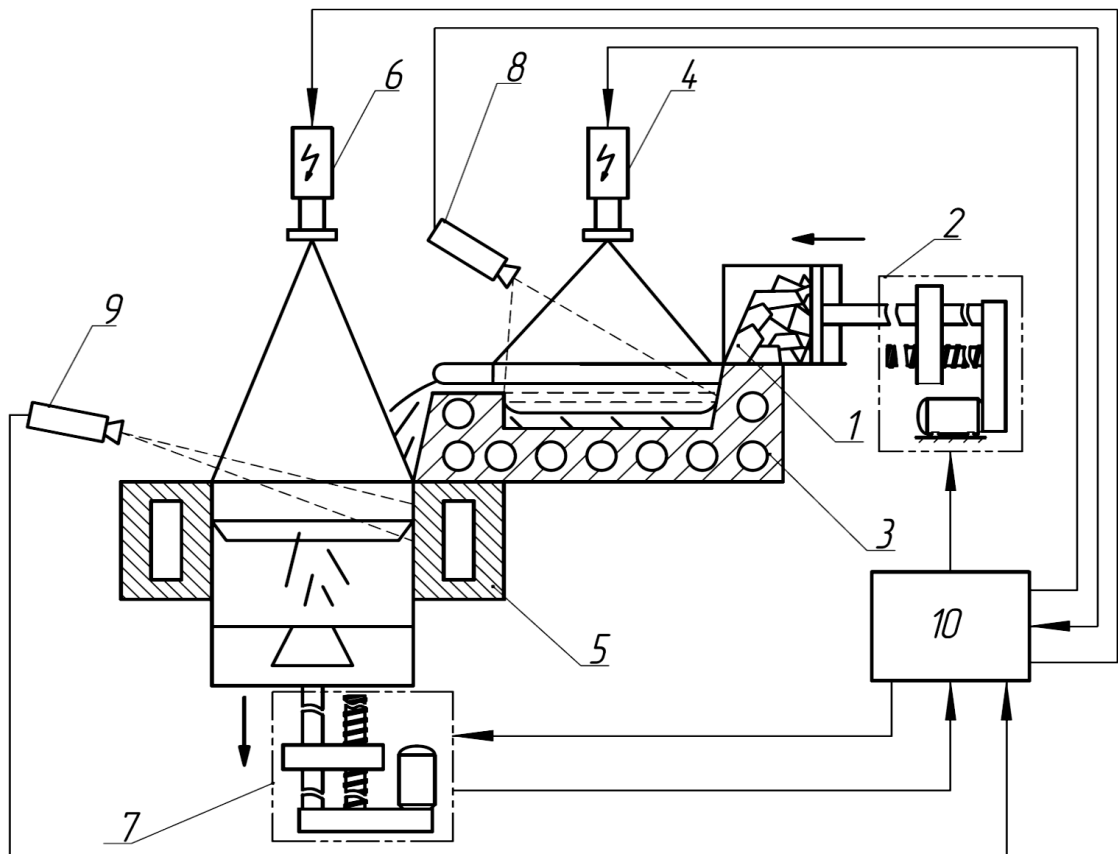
Принципова схема механотронної системи керування виплавою титану: 1 – бункер з шихтою; 2 – механізм подачі шихти; 3 – ПЄ; 4,6 – ЕПГ; 5 – кристалізатор; 7 – механізм витягування зливку; 8 – тепловізор; 9 – відеокамера рівня розплаву; 10 – блок керування
